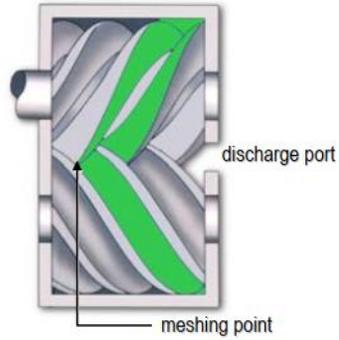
ponto de engrenamento de rotores helicoidais do compressor.
